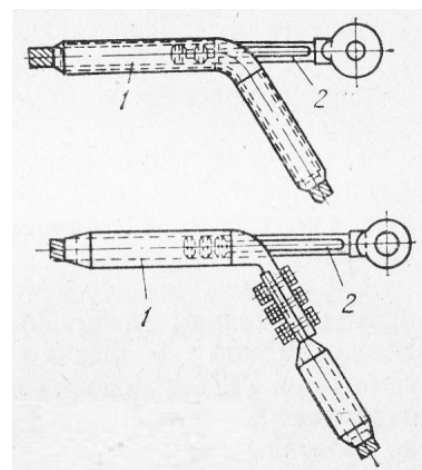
неразъёмный (вверху) и разъёмный (внизу) прессуемые зажимы
